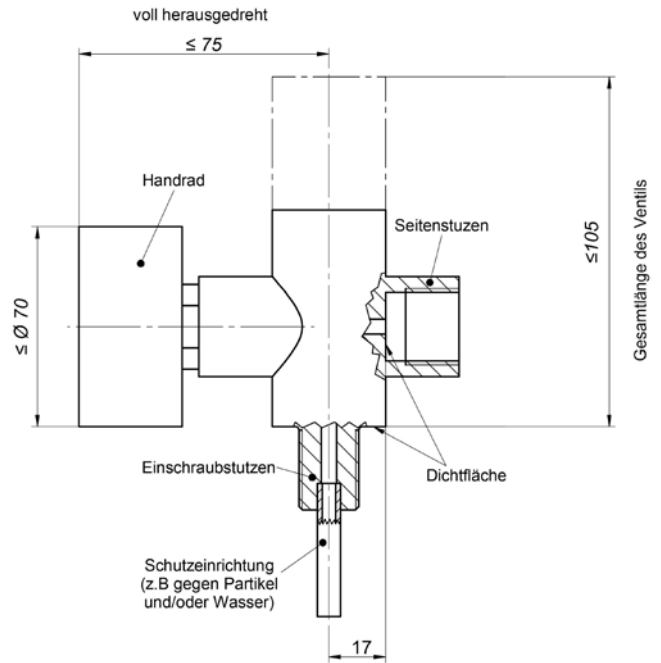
Druckgasbehälterventil Typ 2 (alle Maße in mm)
